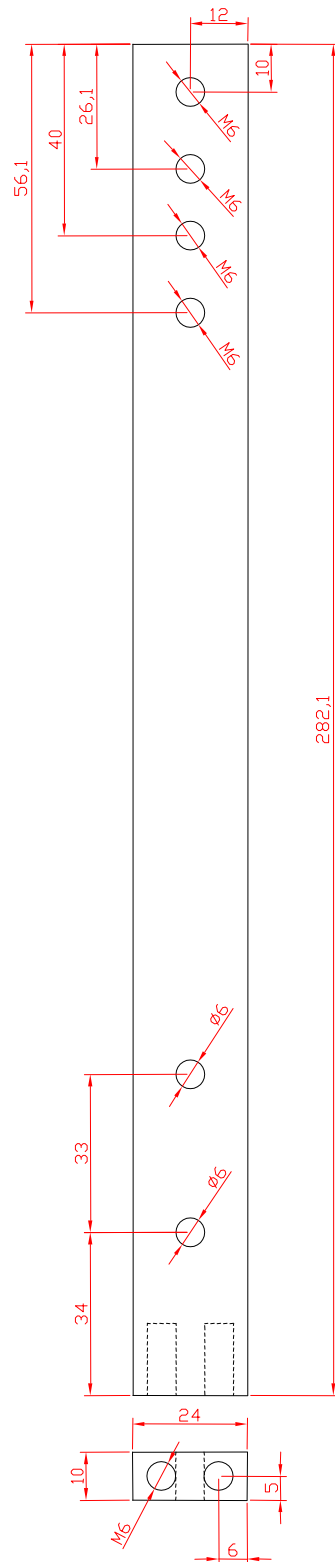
Vista frontal y de la base de los soportes verticales.
